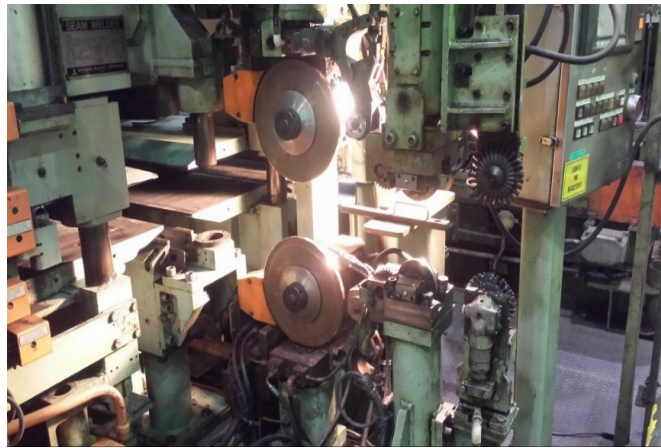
Equipamento utilizado nesse trabalho para a soldagem por costura.
